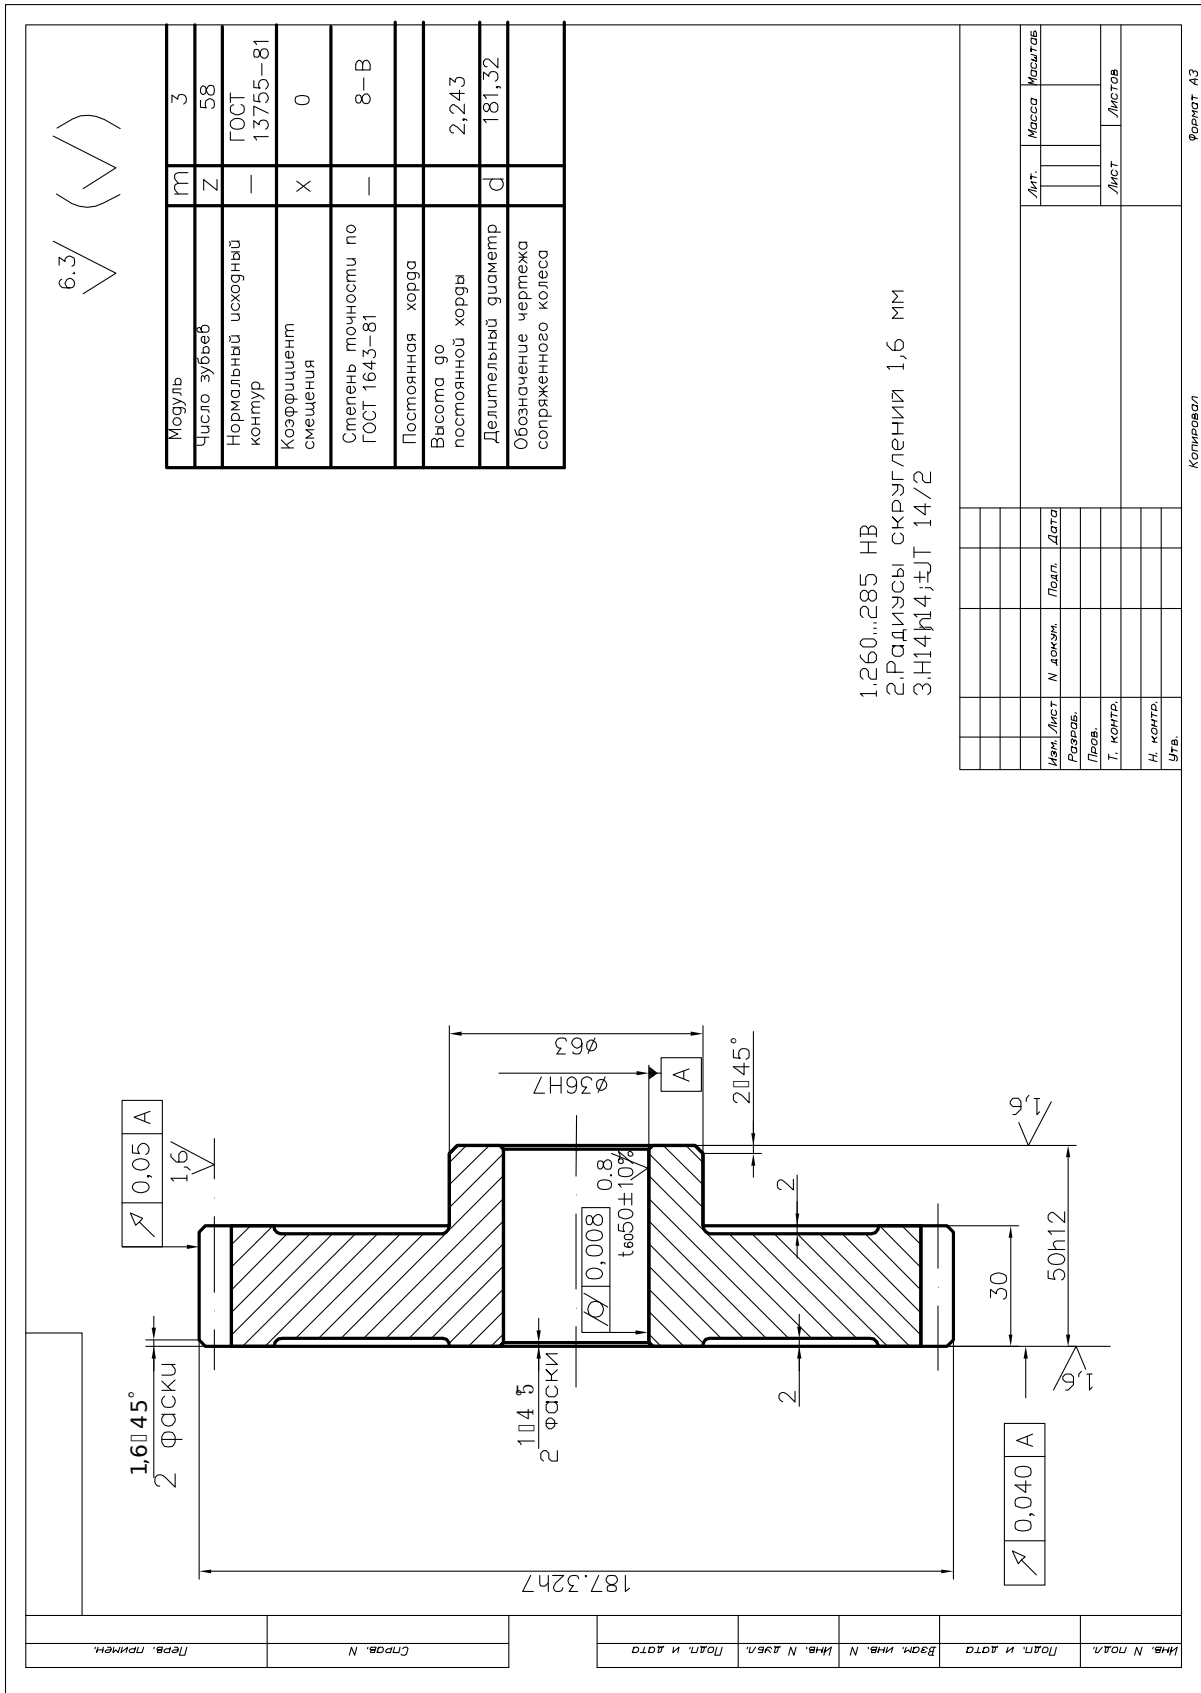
Рабочий чертёж колеса цилиндрического прямоугольного
